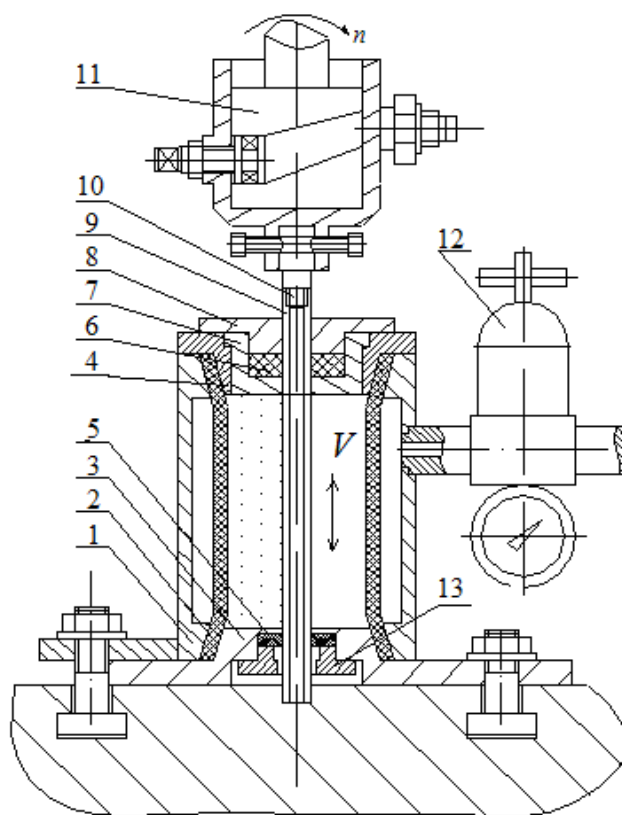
Установка для камерной абразивной обработки плоских поверхностей деталей
